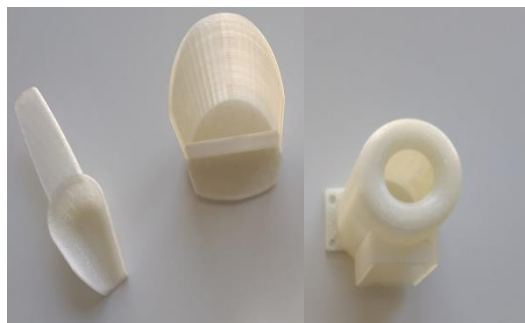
Útiles fabricados mediante impresión 3D con las bobinas 1 y 2 Fuente Propia
